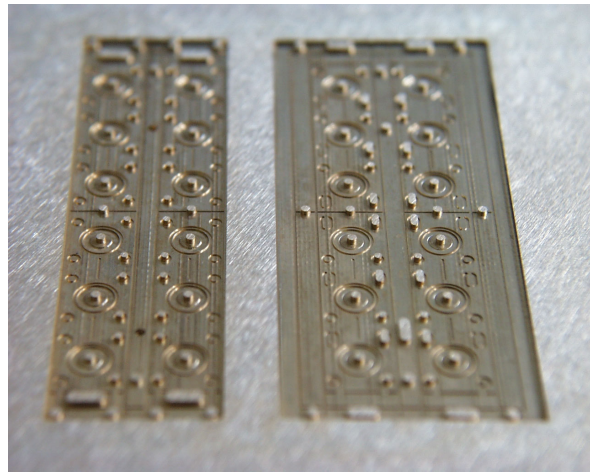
Detailzeichnung aus dem Abformwerkzeug,
